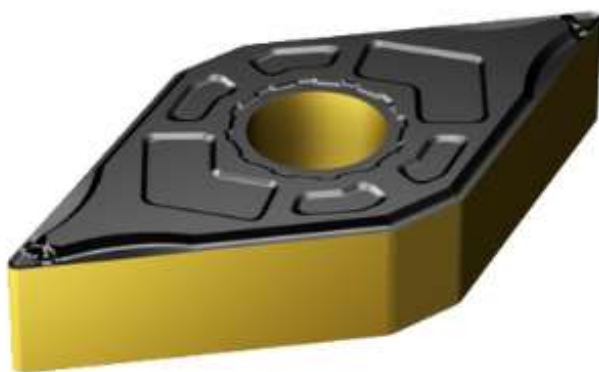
Пластина DNMG 11 04 04-LC 4415
